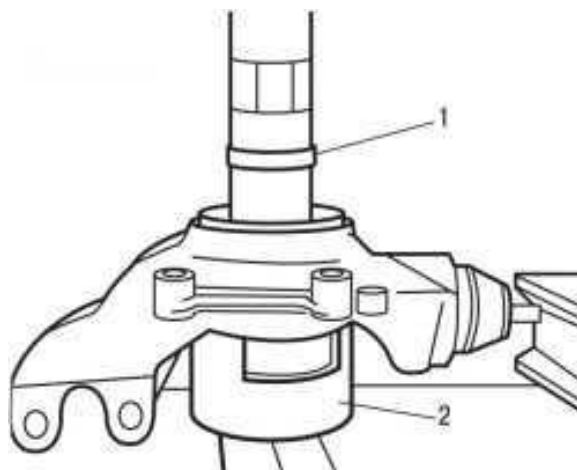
Випресування підшипника з поворотної цапфи:
